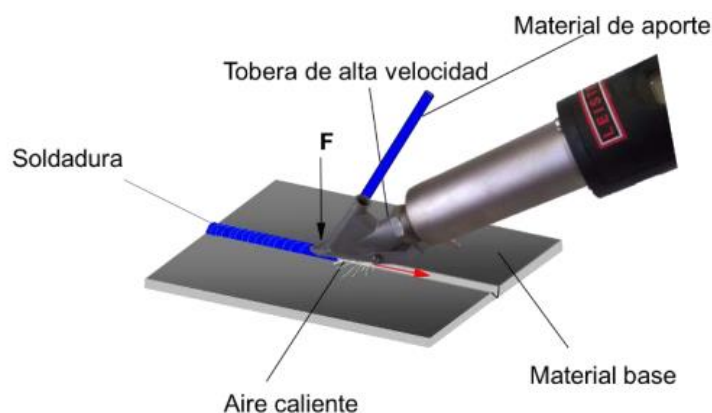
Esquema procés soldadura per aire calent amb punta ràpida [27]
